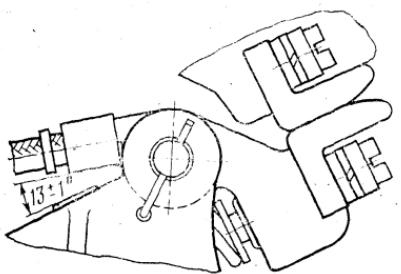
Определение провала контактов ПК и КЭ-1 по углу поворота держателя контакта
